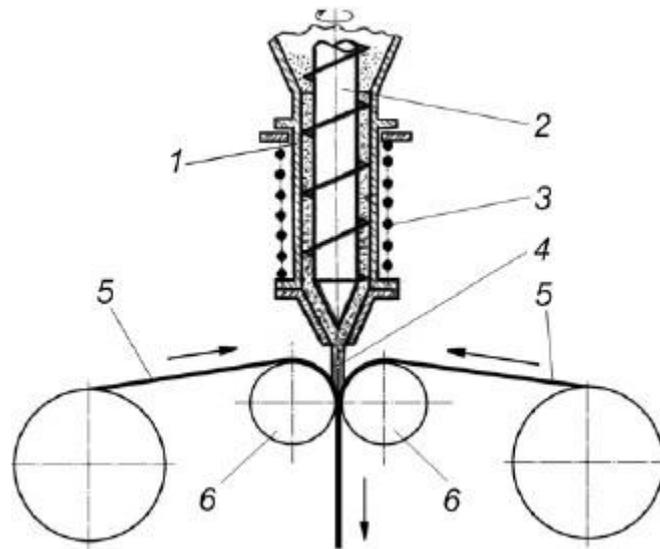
Схема бесконтактной экструзионной сварки полимерных пленок: 1 – корпус экструдера; 2 – шнек; 3 – нагреватель; 4 - присадка из экструдера; 5 – свариваемые пленки; 6 – прижимные ролики
